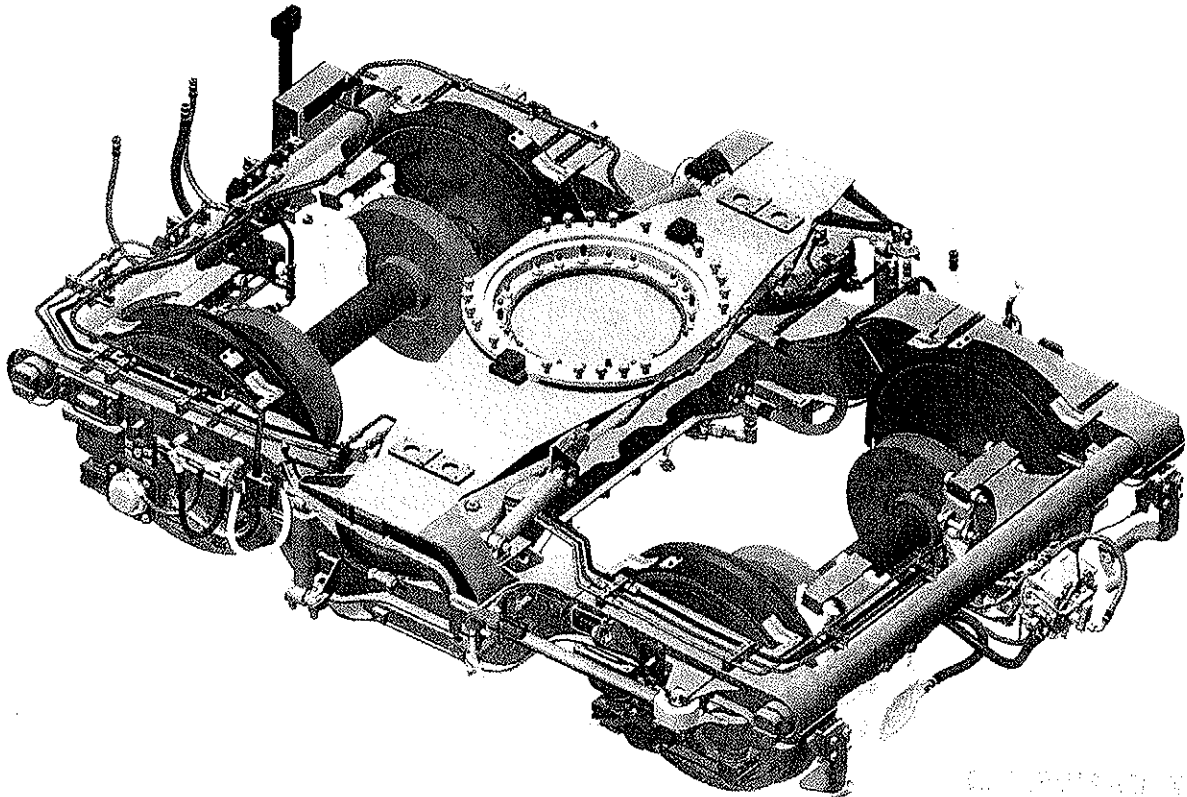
Vista isométrica de la parte superior del bogie remolque
